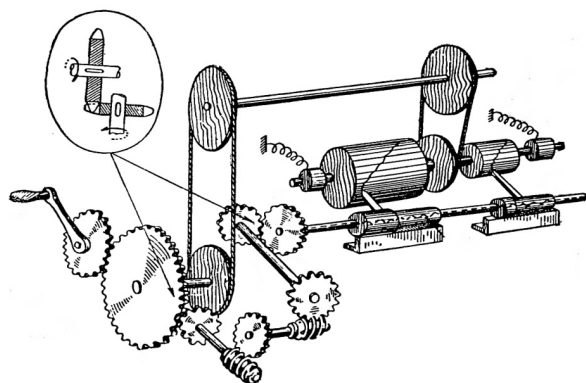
Привод токарного верстата А. Нартова із самохідним супортом
